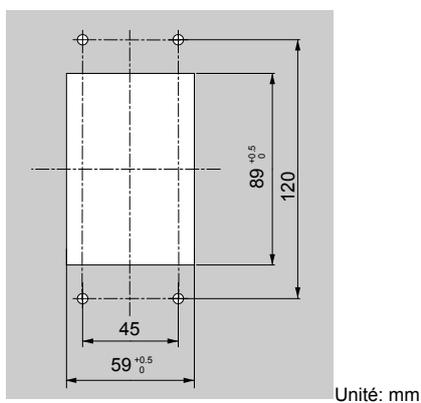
Dimensions de découpe du panneau (installation interne/encastrable)
